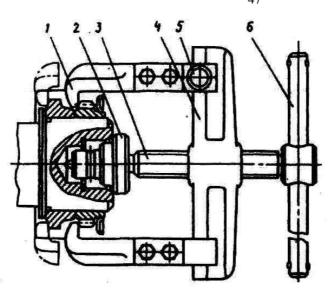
Снятие шестерни и заднего противовеса коленчатого вала двигателя КамАЗ-740 универсальным винтовым съемником: I — захват; 2 — сменяемый наконечник; 3 — винт силовой; 4 — траверса; 5 — стопор; 6 — рукоятка
